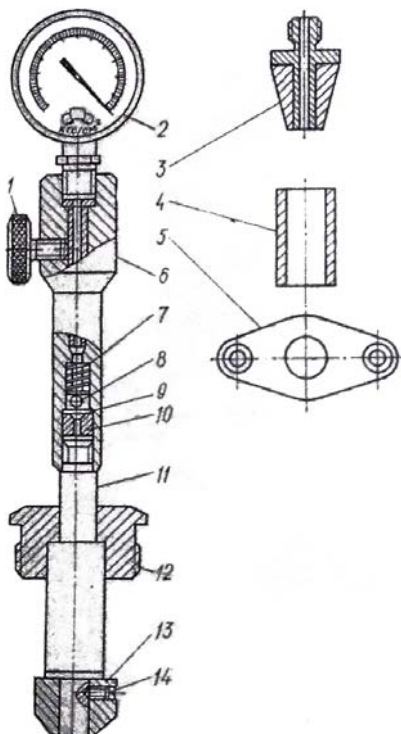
Компресиметр КИ-861: 1 – вентиль; 2 – манометр; 3,13 – наконечники; 4 – втулка; 5 – фланець; 6 – корпус; 7 – пружина; 8 – кульковий клапан; 9 – гумова прокладка; 10 – регулювальний гвинт; 11 – трубка; 12 – з'єднувальна муфта; 14 – установочний гвинт.
